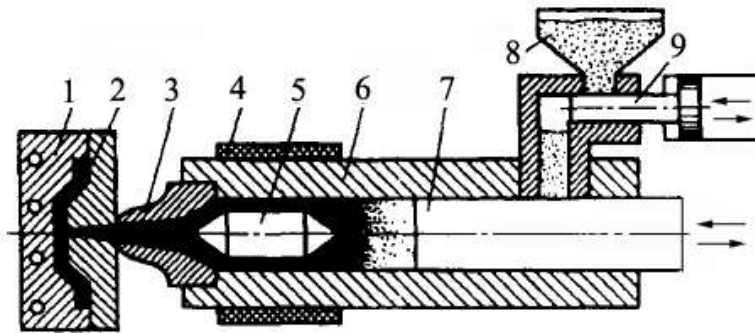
Схема виготовлення деталей з ПКМ методом лиття під тиском
